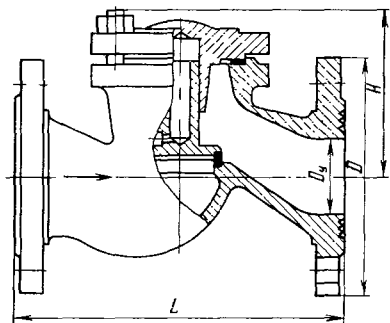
Клапан обратный подъемный типа 16с13иж
